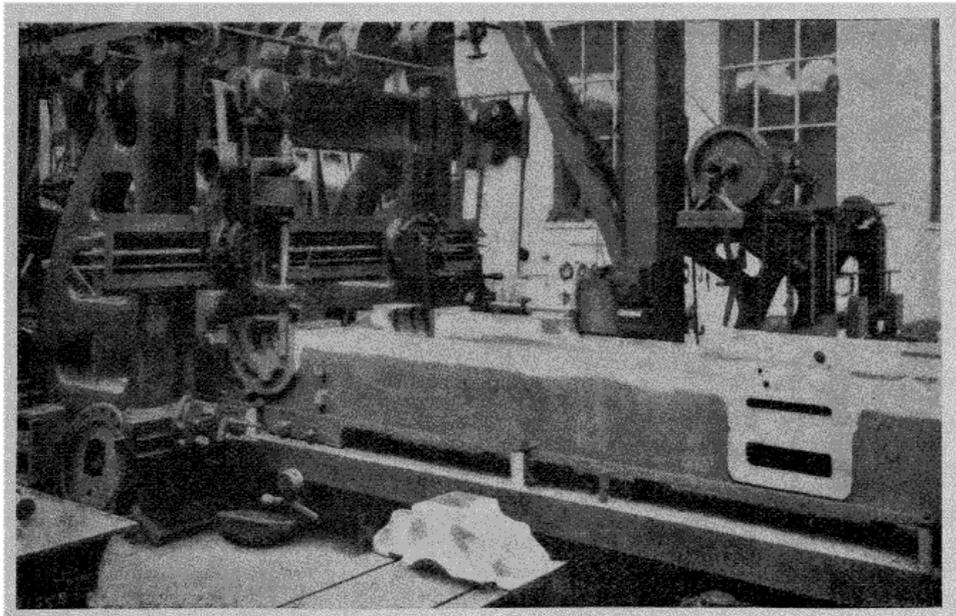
Usinage d'un bâti du type fig. 17 sur une raboteuse.
